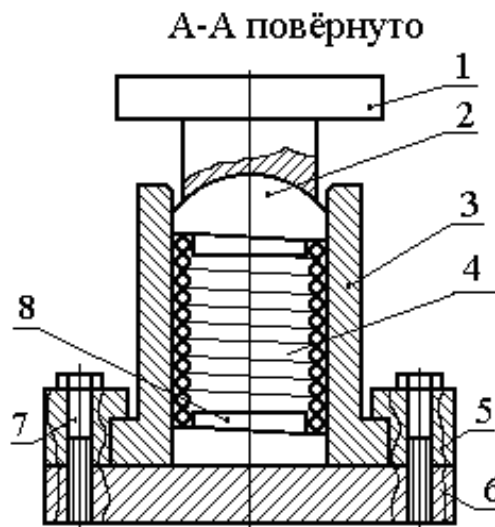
Сечение А-А устройства по пат. RU 2251036 [96]
